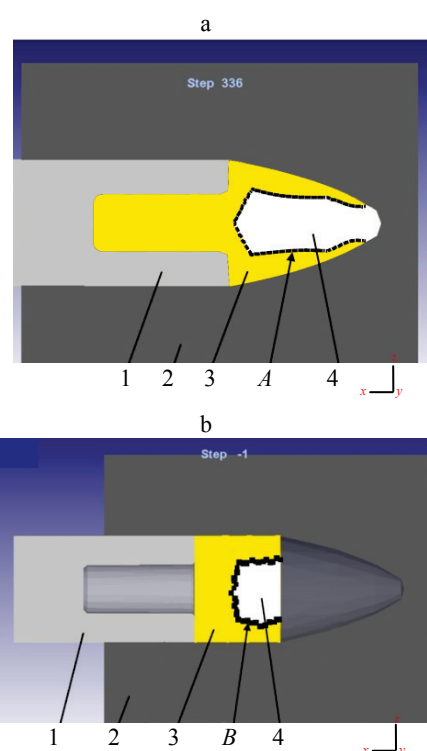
Модель пластического течения продеформированной заготовки: 1 – пуансон; 2 – полуматрица; 3 – конструкционная сталь; 4 – быстрорежущая сталь
